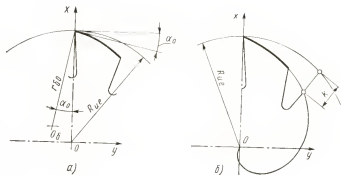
Параметры задней поверхности дисковых фрез с затылованным зубом
